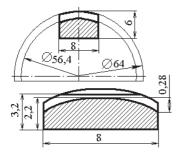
Размеры и схема вырезки продольного образца из шпильки M64x6, длина образца l=60...80 мм
